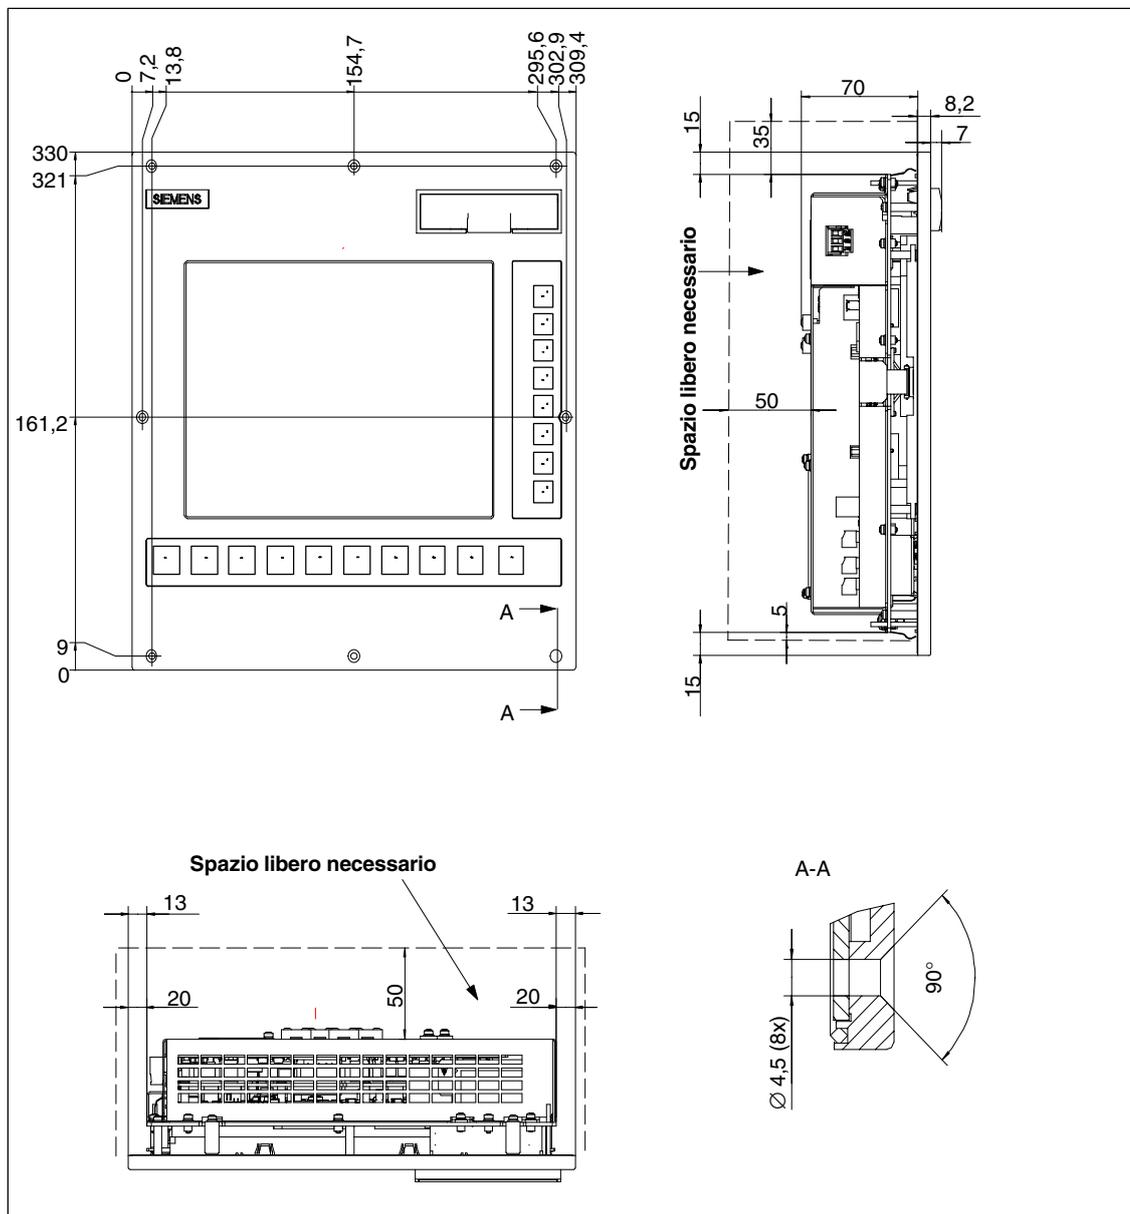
Disegno quotato del pannello di servizio CNC
